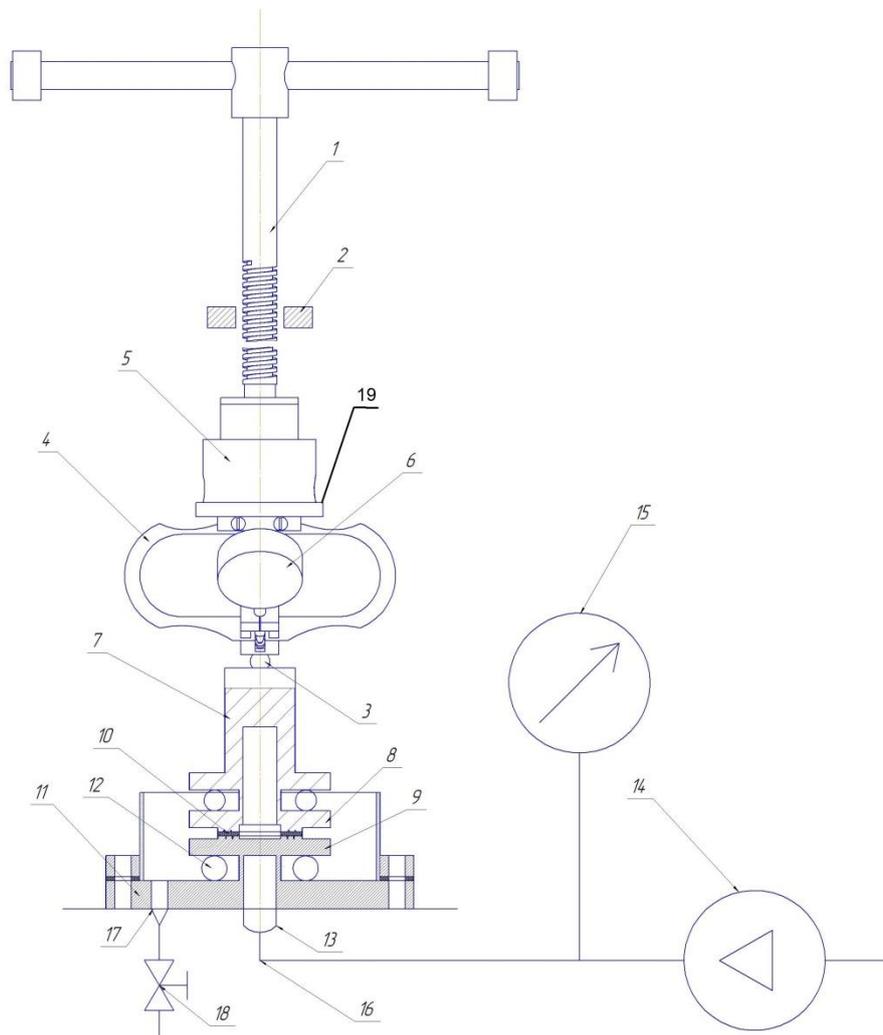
Стенд для испытания фланцевого соединения на герметичность 1-винт, 2-неподвижная гайка, 3-упорный подшипник, 4-упругий элемент, 5-головка, 6-индикатор часового типа, 7-центратор, 8-верхний фланец, 9-нижний фланец, 10-прокладка, 11-ванна, 12-стальные шарики, 13-цилиндрический патрубок, 14-компрессор, 15-манометр, 16-гибкий шланг, 17-выпускное отверстие, 18-вентиль, 19-платформа.
